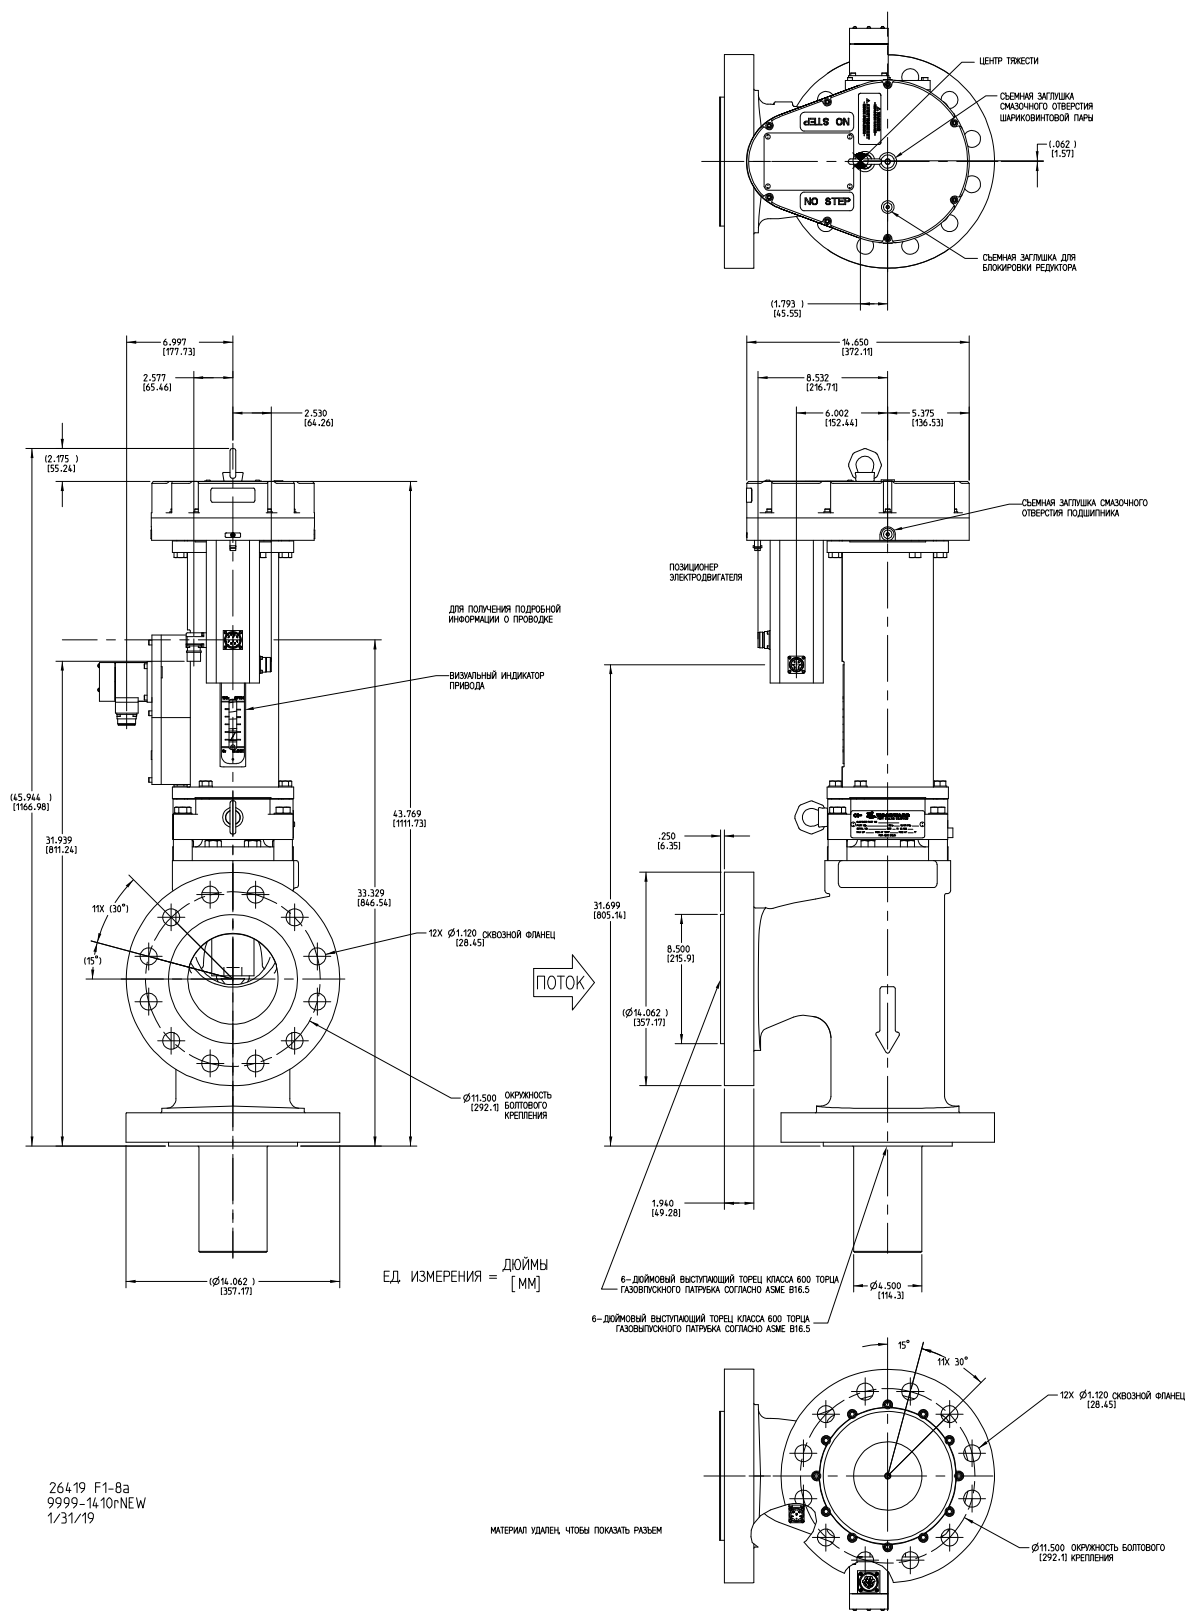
а. Габаритный чертеж (6-дюймовый клапан LESV класса 600)
